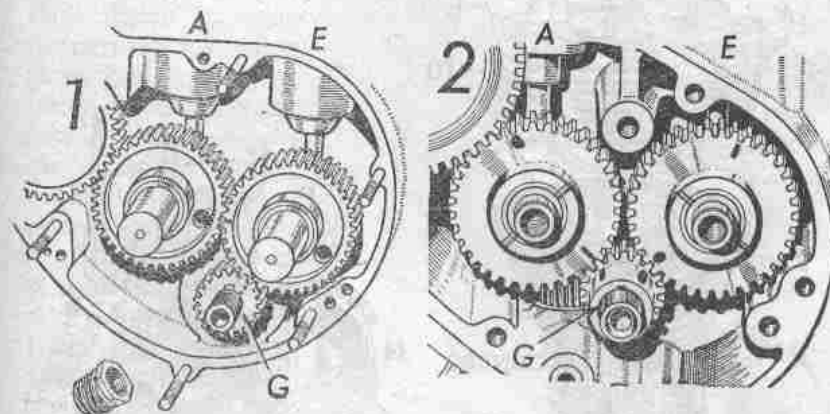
Engranajes de la distribución y marcas para su montaje.
